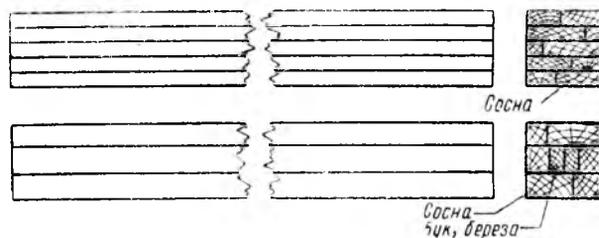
Два варианта клееных заготовок для валиков сноповязалок
